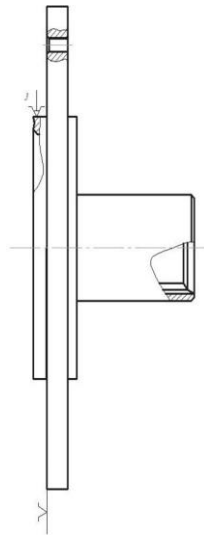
Фланець ведучої частини маточини колеса
